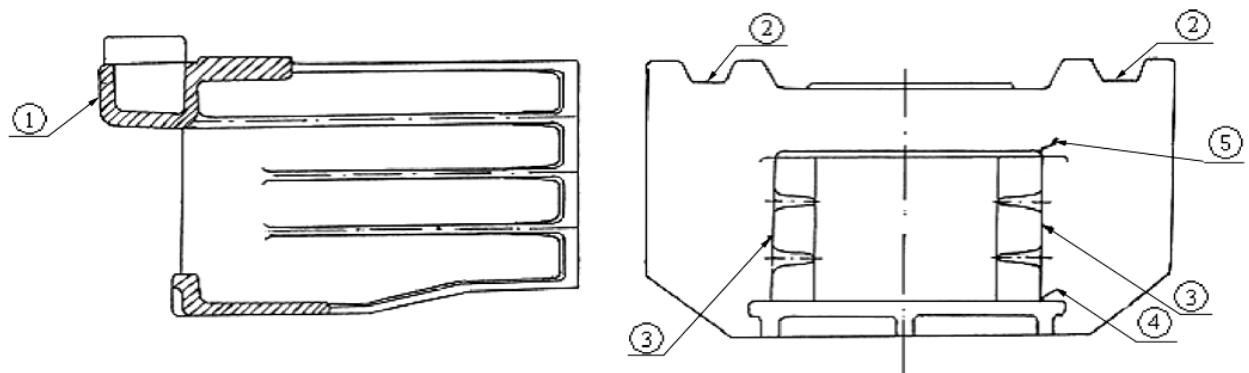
Дефекты упора переднего для пассажирских вагонов, ремонтируемые сваркой или наплавкой
